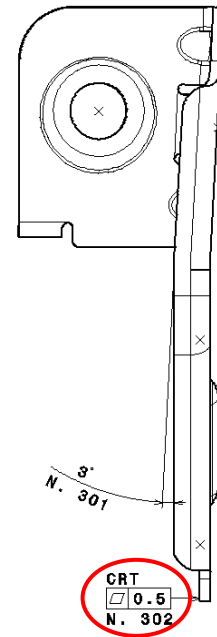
Tolerância de planeza “Filler Head Bracket”
